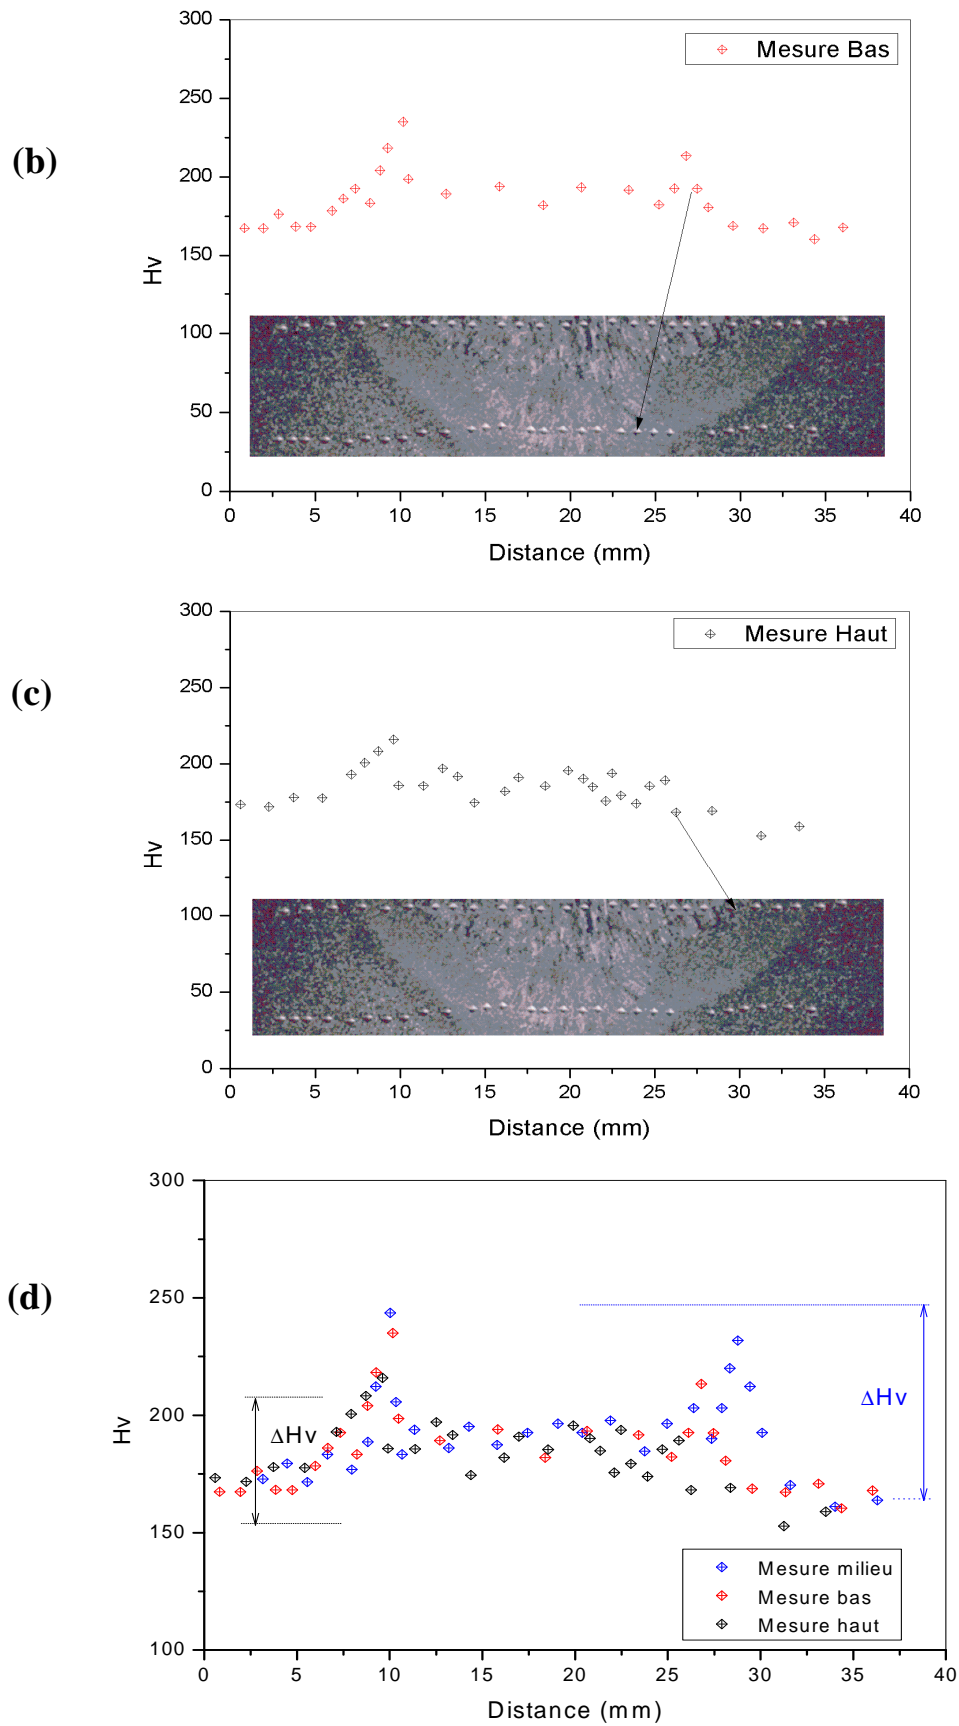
Filiations de dureté effectuées sur le joint soudé en surface et transversale perpendiculaire au cordon de soudure.
